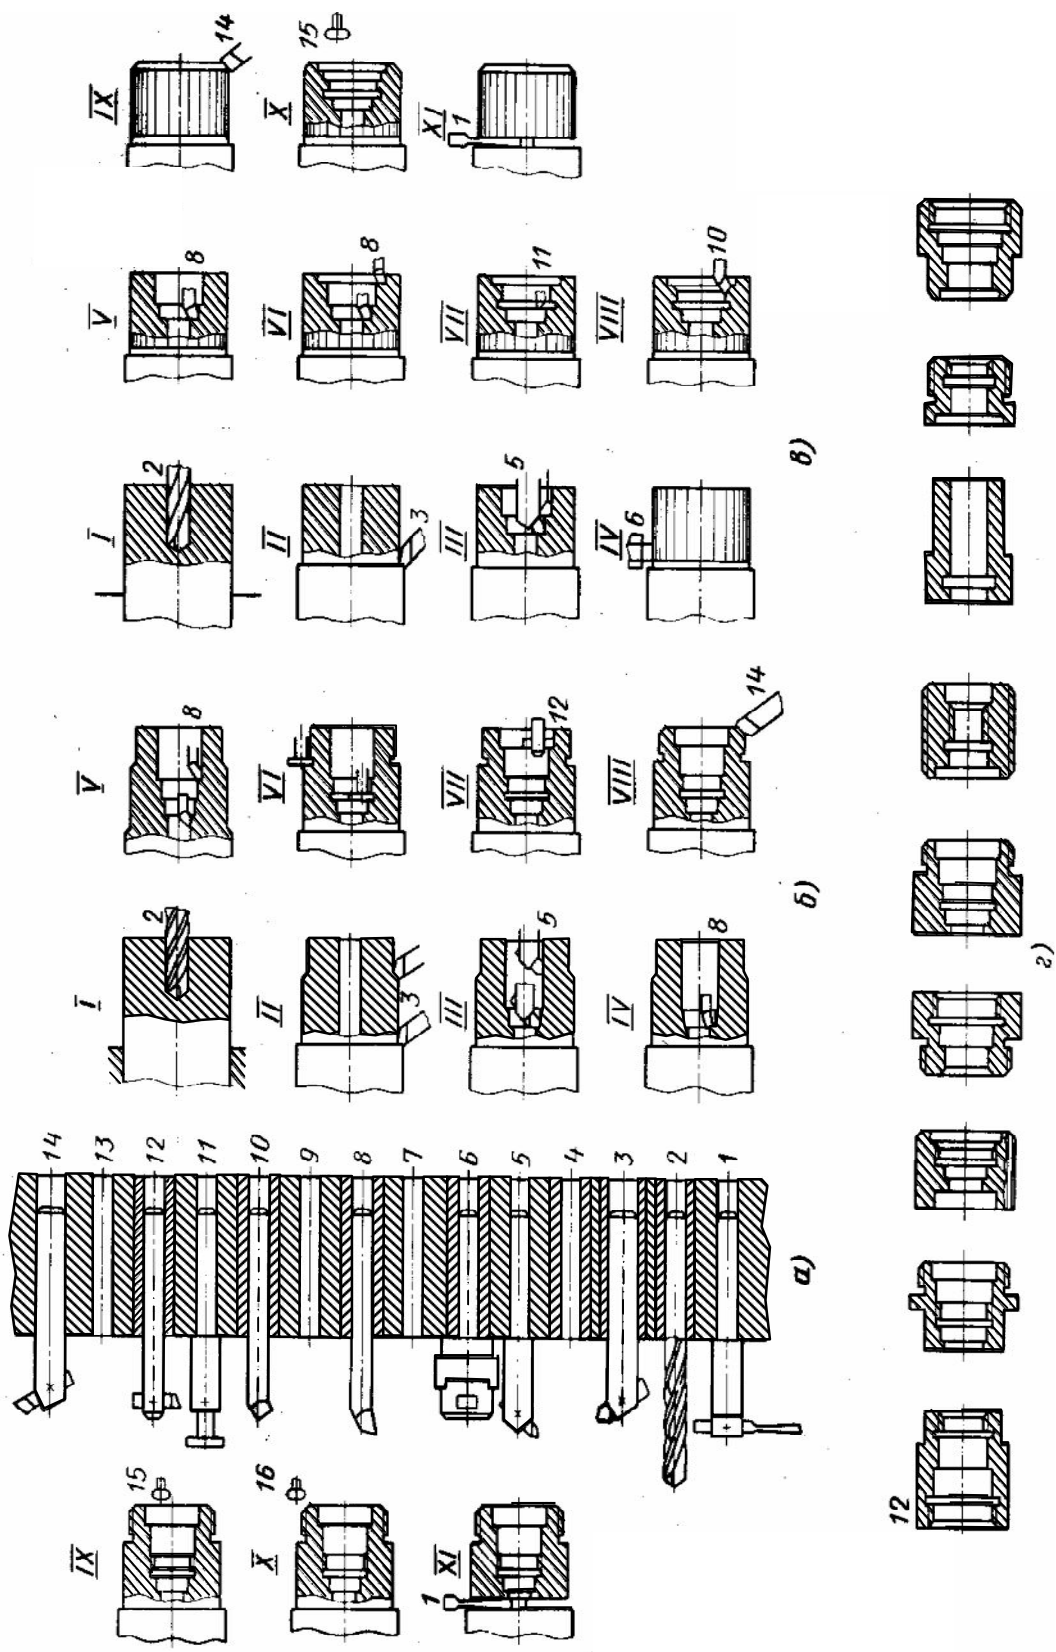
Схеми налагодження револьверної головки для групової обробки заготовок: а – розгортка револьверної головки з комплектом інструмента; б, в - схеми виконуваних переходів обробки; г – ескізи типових деталей. I - XI - переходи обробки; 1 – 16 - позиції інструментів в револьверній головці
